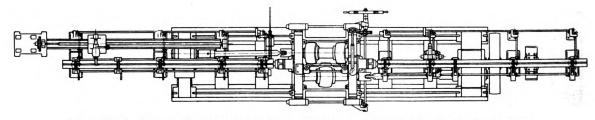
bis 12. Schwere Friemelmaschine für das Richten von Edelstahl bis 150 mm Durchmesser.
